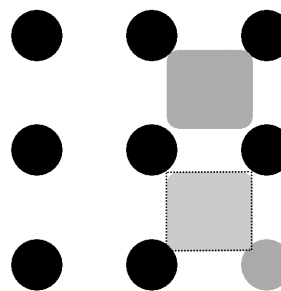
Двухполюсник, расположенный под контактами BGA, блокирует ячейки справа и слева
